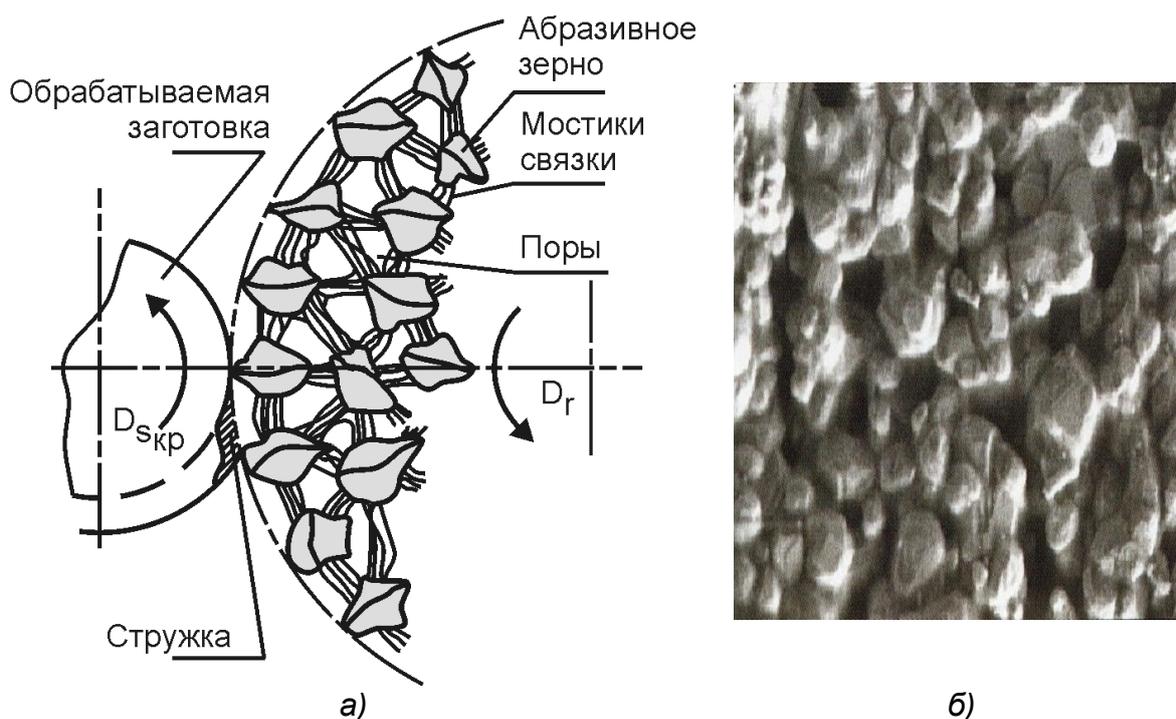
Схема конструкции (а) и поверхность (б) абразивного инструмента
